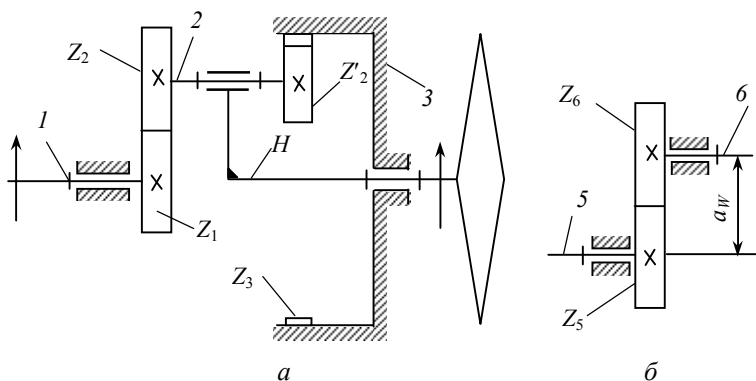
Схема редуктора (*а*) и механизма привода топливного насоса (*б*) авиационного двигателя
